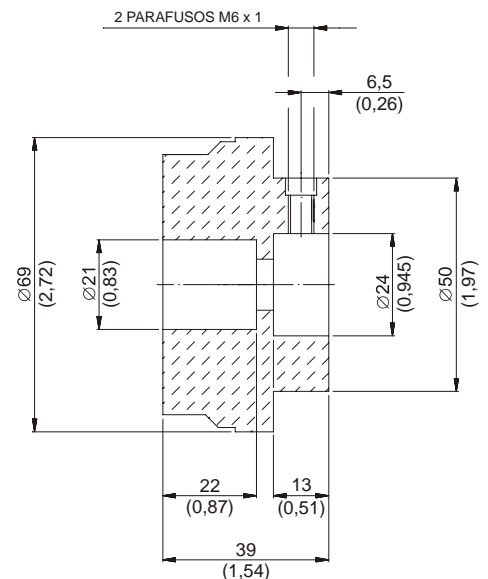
Desenho Dimensional do TP302 e do Ímã
